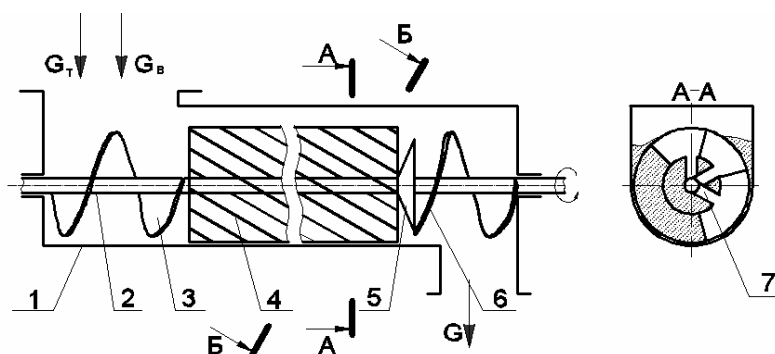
Схема смесителя для подготовки торфомассы к формированию
